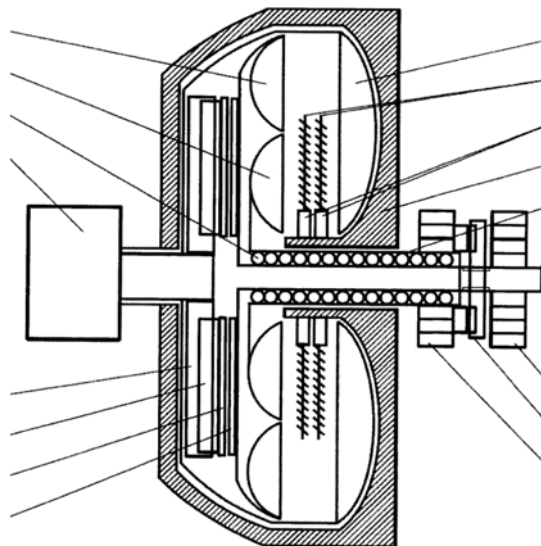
Схема гидротрансформатора гидромеханической передачи для раздельного привода ведущих мостов колесного движителя
